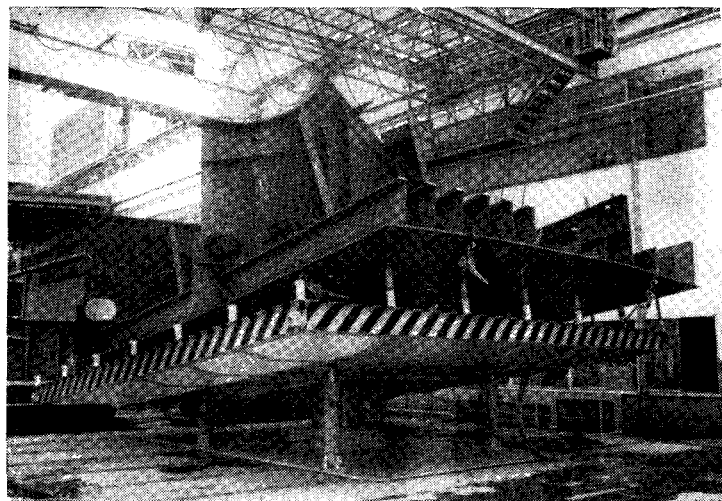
Позиционер для сварки криволинейных секций.
